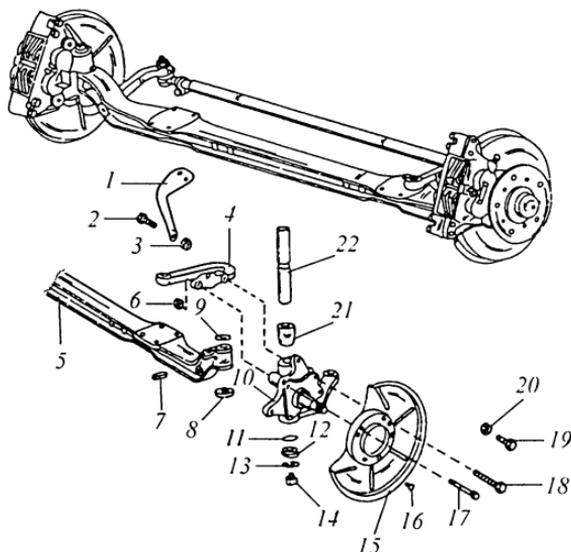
Передний мост микроавтобуса Mercedes 1 — удерживающий уголок; 2, 17, 18, 19 — болты; 3, 6, 20 — гайки; 4 — рычаг поворотного кулака; 5 — балка моста; 7 — штифт; 8 — упорный подшипник; 9 — распорная шайба; 10 — поворотный кулак; 11 — уплотнительное кольцо круглого сечения; 12 — чехол; 13 — стопорное кольцо; 14 — масленка; 15 — шиток; 16 — заклепка; 21 — втулка поворотного кулака; 22 — шкворень поворотного кулака
